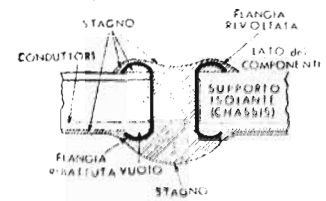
Riparazione della rottura del rame intorno ad un occhio. Lo stagno applicato deve ricoprire interamente l'occhietto, dal lato della ribaditura, onde assicurare il contatto.
